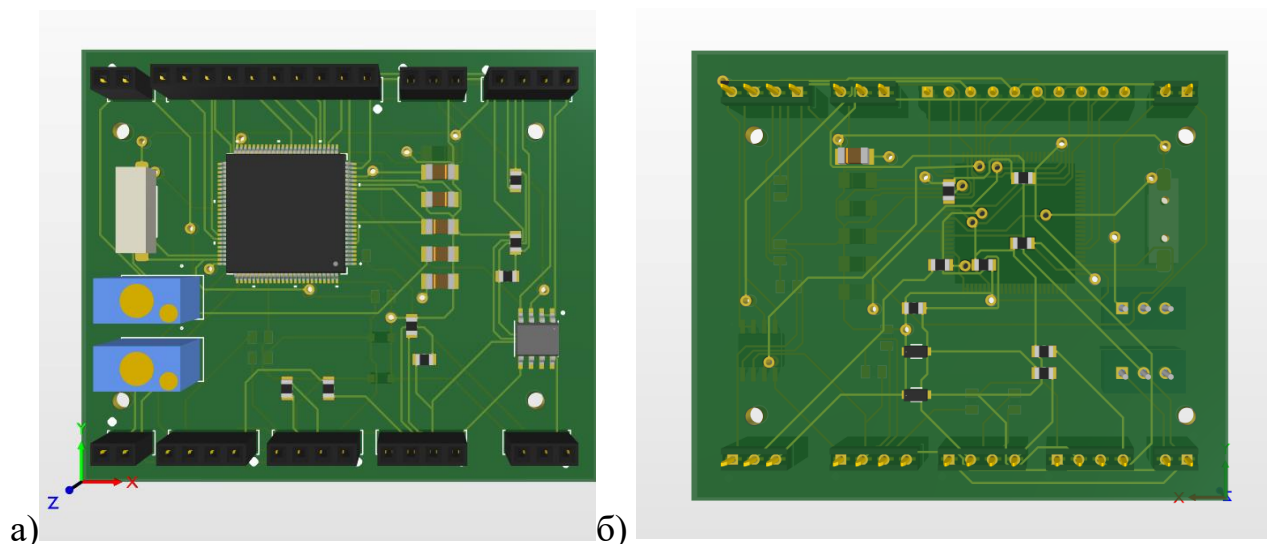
Друкований вузол, а) Вид зверху, б) Вид знизу
